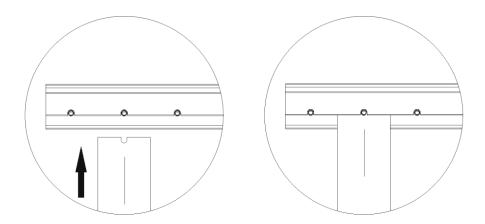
Einsetzen des Mono Connector Boards, exemplarisch
